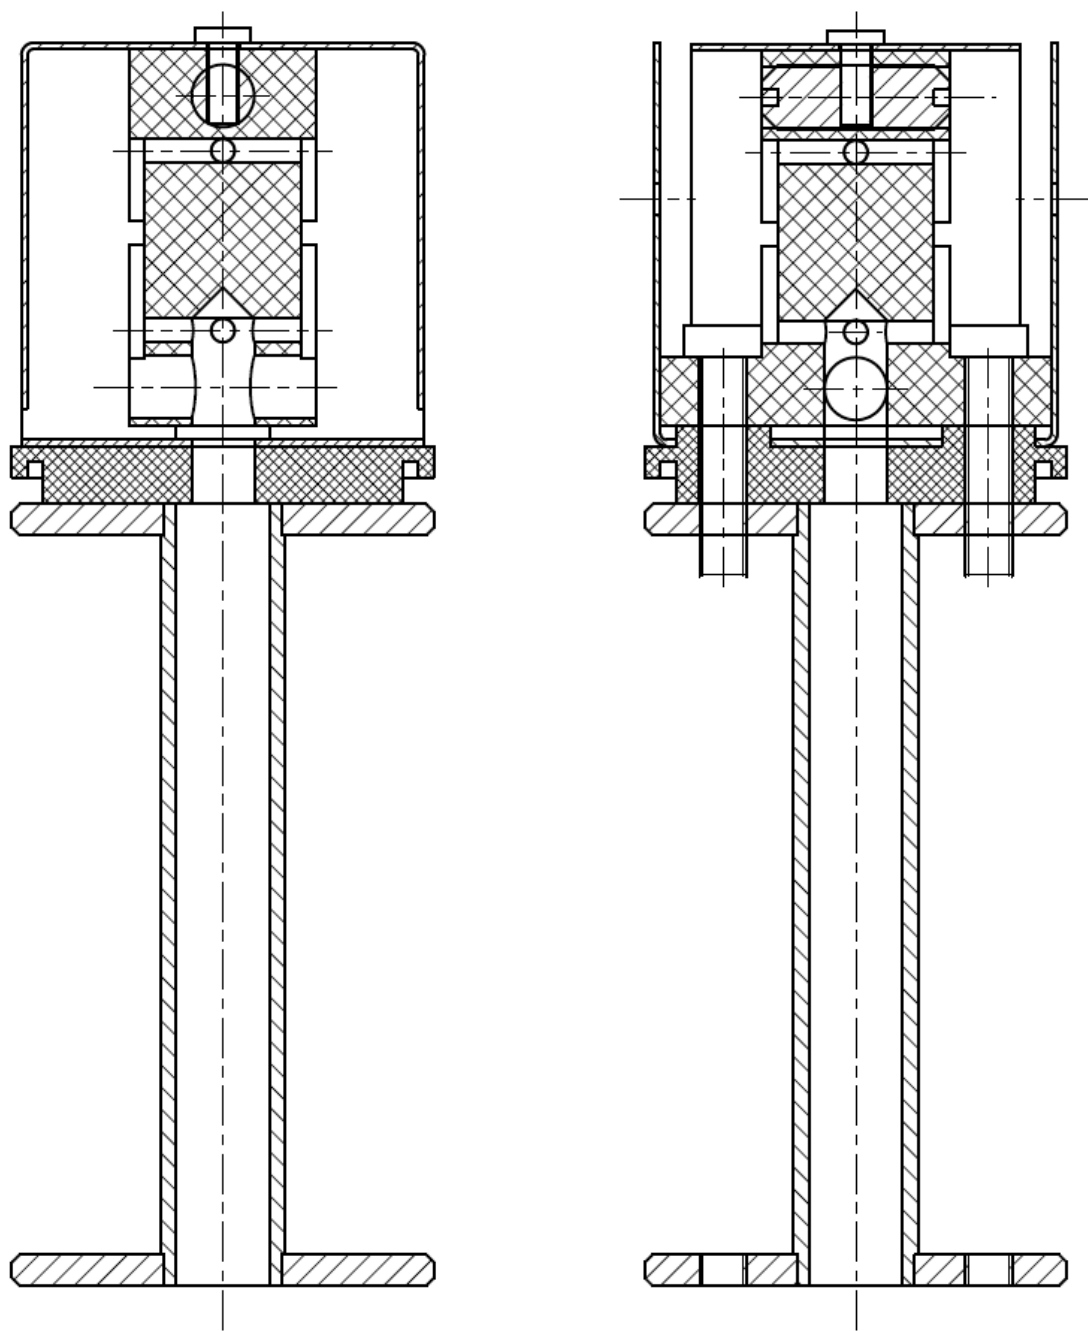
Сборочный чертеж датчика новой магнитной диагностики
